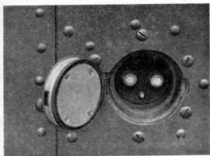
Установка газоотвода контейнера аккумулятора за борт вертолета.
